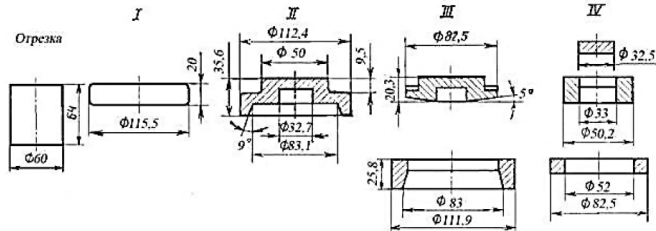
Совмещенная штамповка двух деталей от одной заготовки на автомате фирмы «Хатебур» АМР 70
